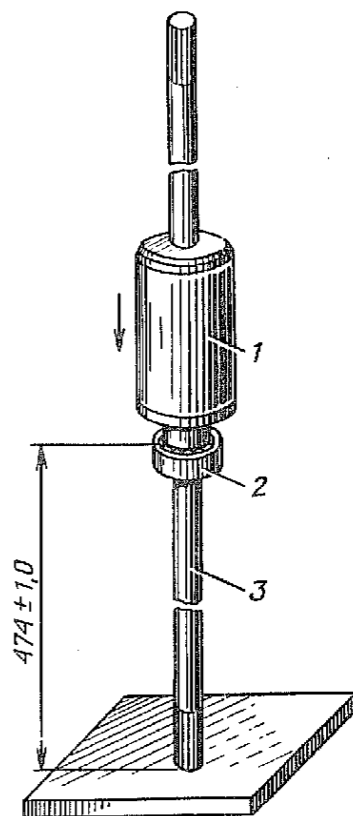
Спрессовка среднего подшипника с приводного вала:
